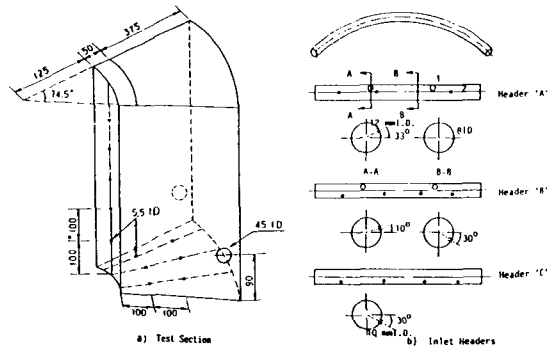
중수 탱크내 유동장 측정을 위한 Test Section
